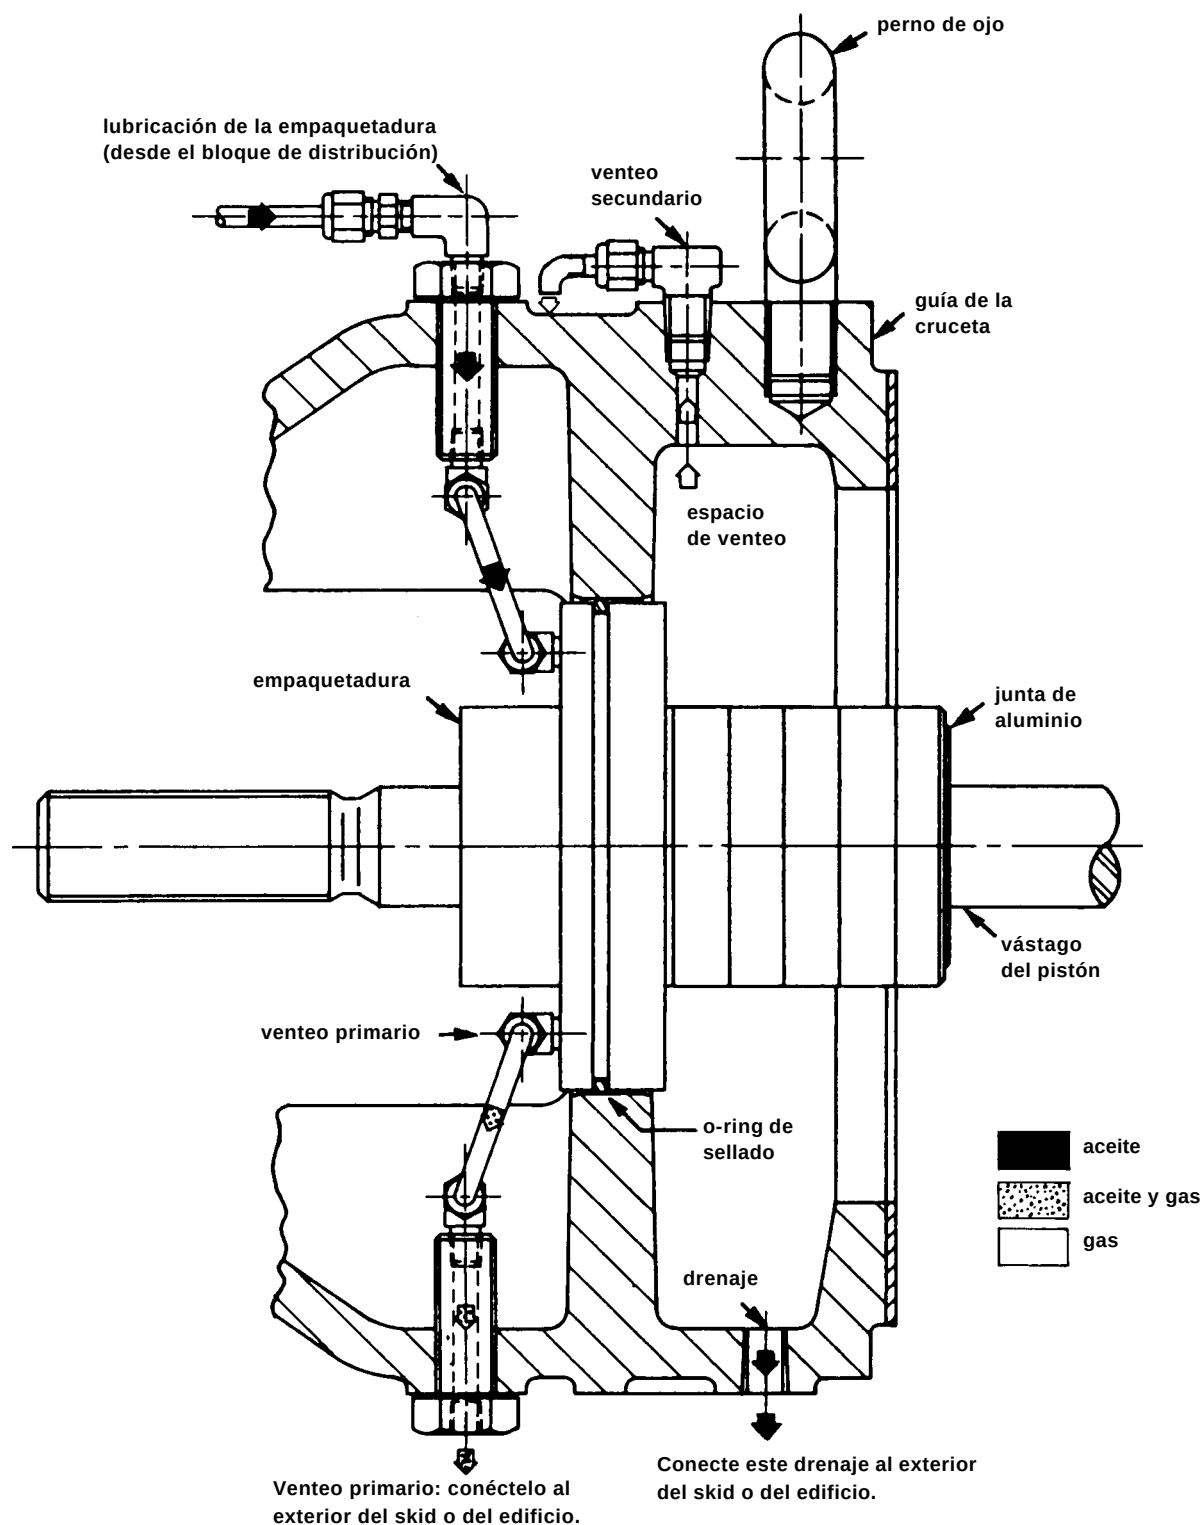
EMPAQUETADURA, TUBERÍA Y VENTEO DE LA PIEZA ESPACIADORA
